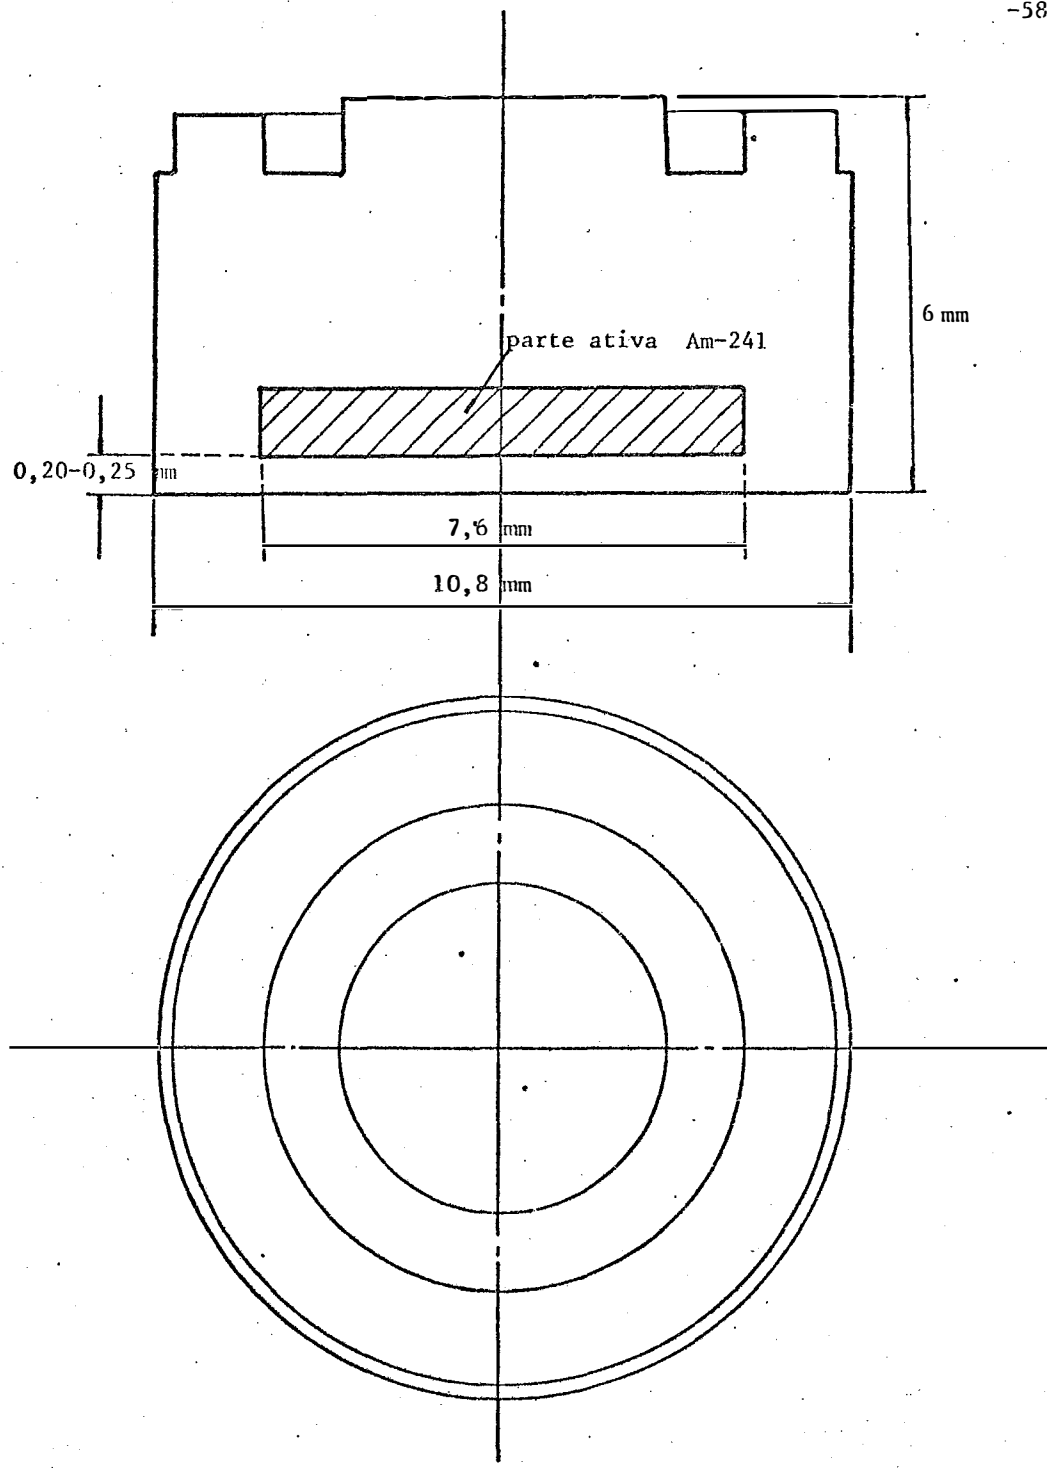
Desenho esquemático da fonte de Am-241 (dimensões em milímetros).
